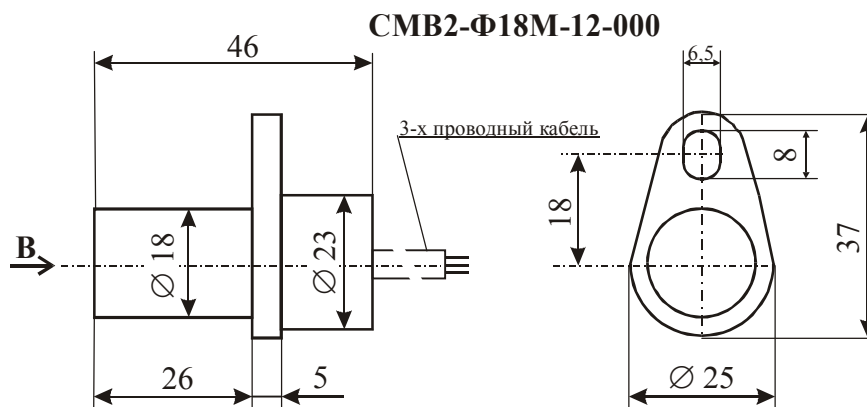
Внешний вид и габаритные размеры датчиков типа СМВ2-Ф18М-12-000
